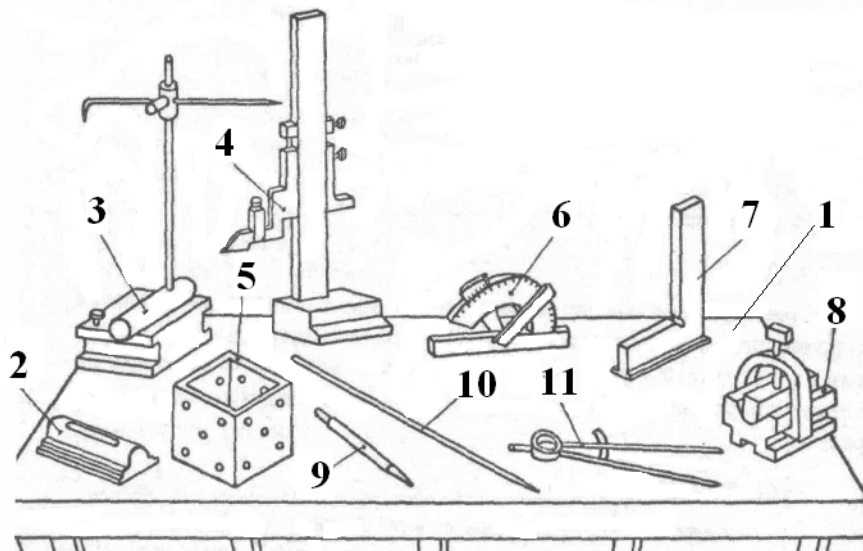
Розмічувальні інструменти: 1 – розмічувальна плита; 2 – рівень; 3 – рейсмус; 4 - штангенрейсмус; 5 - розмічувальний ящик; 6 - кутомір; 7 - косинець; 8 – призма; 9 – кернер; 10 - рисилка; 11 - циркуль
